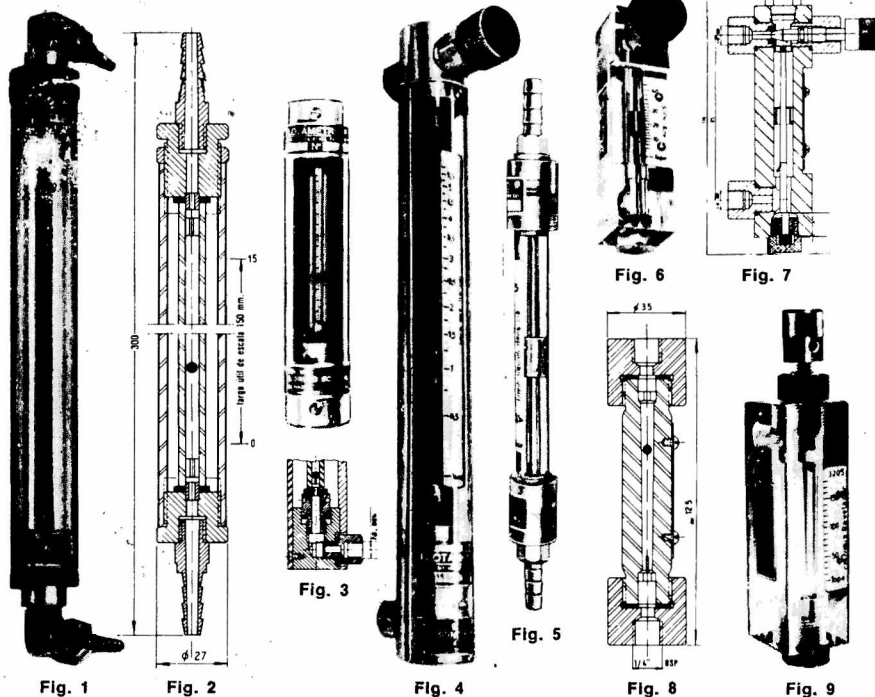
y 4: Tipos U-X/65 y U-R2/15 V con tubo de vidrio BROOKS corto (escala 65 mm) y largo (150 mm) en armazón tubular metálico con protección acrílica. Permiten retirar rápidamente el tubo de vidrio. Exactitud ± 1.3 y 1.5% respectivamente.
